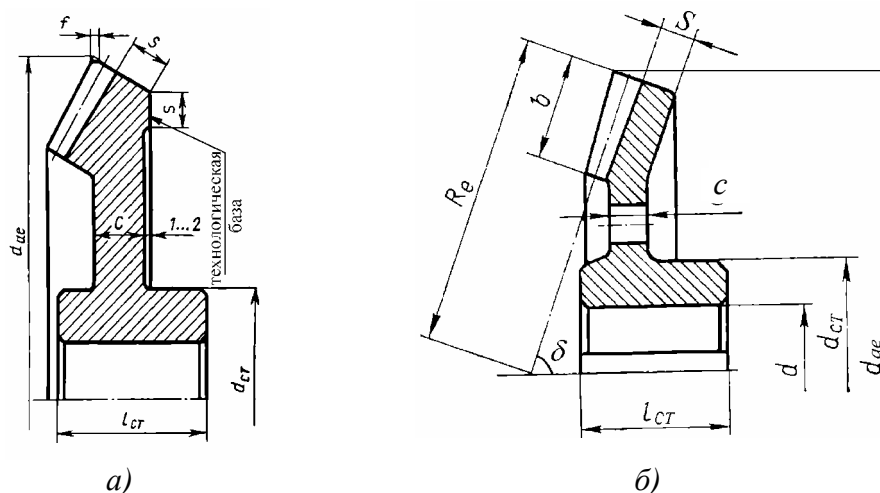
Конструкции кованных и штампованных конических зубчатых колес
